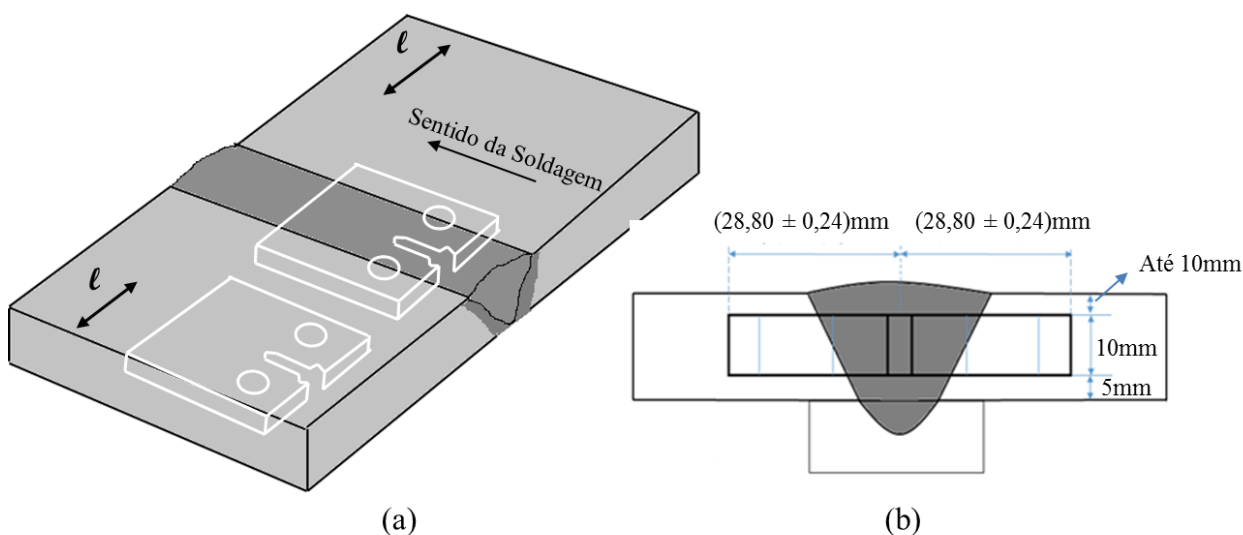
Posicionamento de retirada dos corpos de prova CT de fadiga em relação à chapa soldada; a) posição longitudinal; b) posição transversal.
